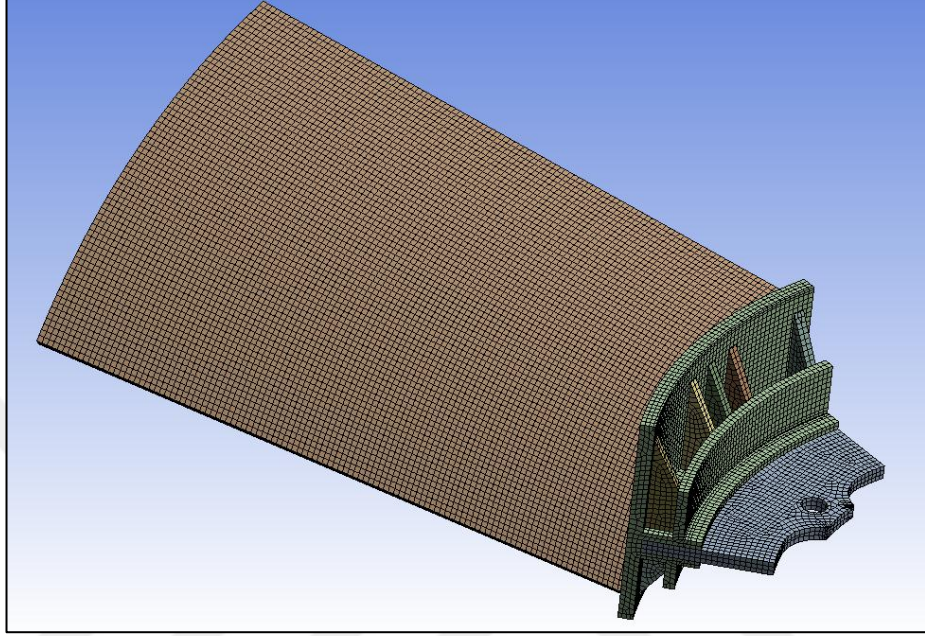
Sistem ayrıklaştırılmasında kullanılan bazı eleman tipleri
